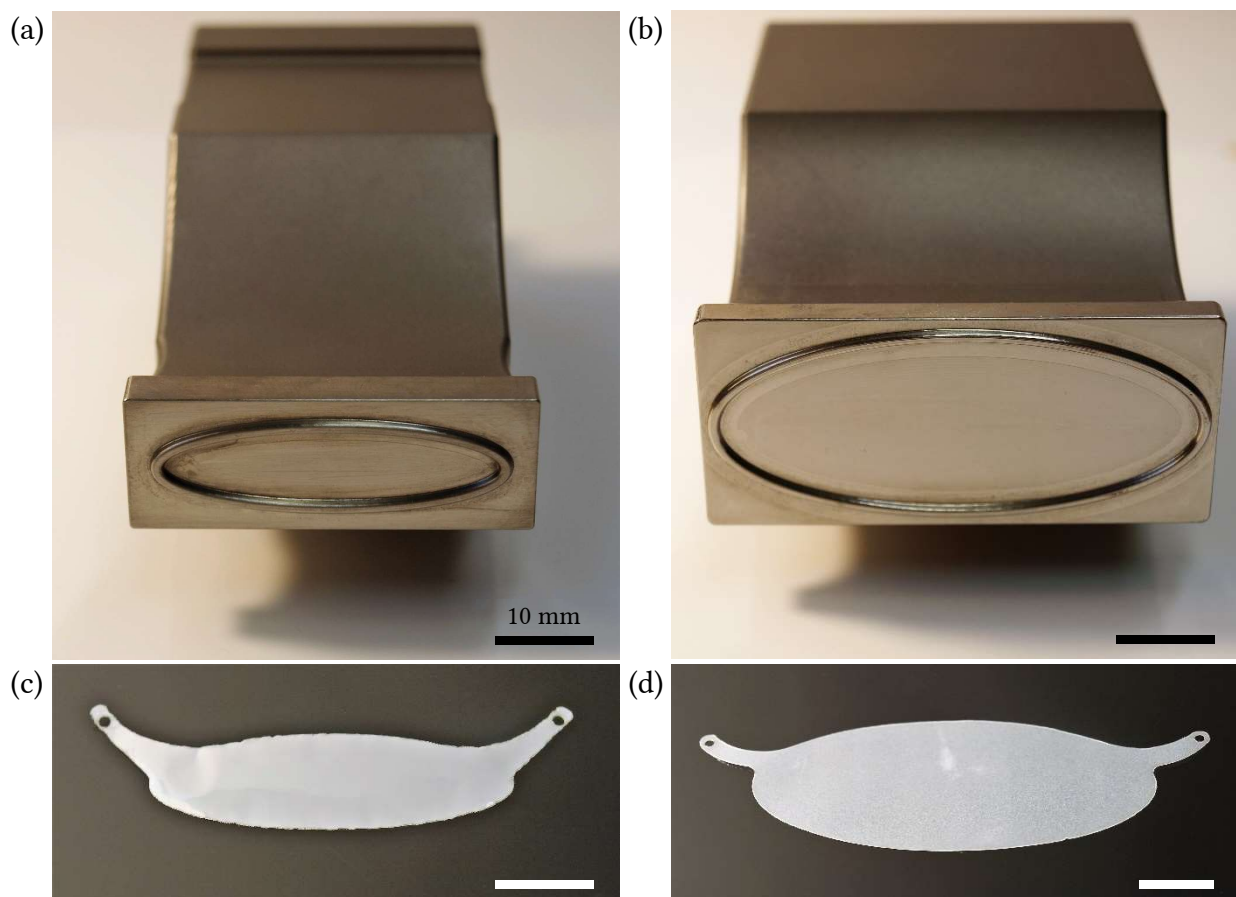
Strukturierte Sonotroden zum Ultraschallschweißen der Membranen auf die Chiphälfte mit Zellkammer. (a) Sonotrode für die Membranen des 100 µl-MBR, (b) Sonotrode für die Membranen des 800 µl-MBR, (c) Membranzuschnitt für den 100 µl-MBR, (d) Membranzuschnitt für den 800 µl-MBR. Der Maßstabsbalken ist einheitlich 10 mm.
